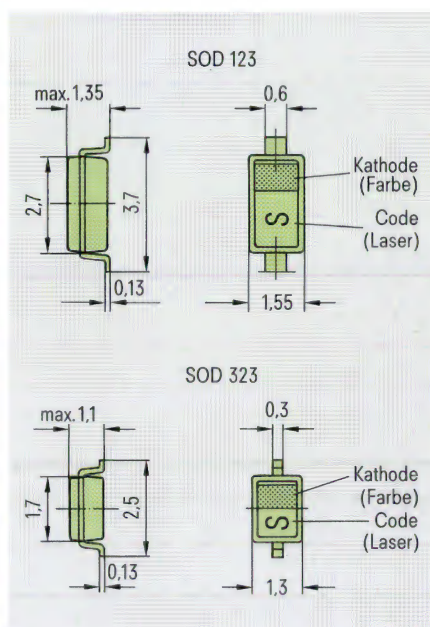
Vergleich der beiden Gehäusebauformen SOD-123 und SOD-323. Die Maße sind ohne in mm Toleranzen angegeben
